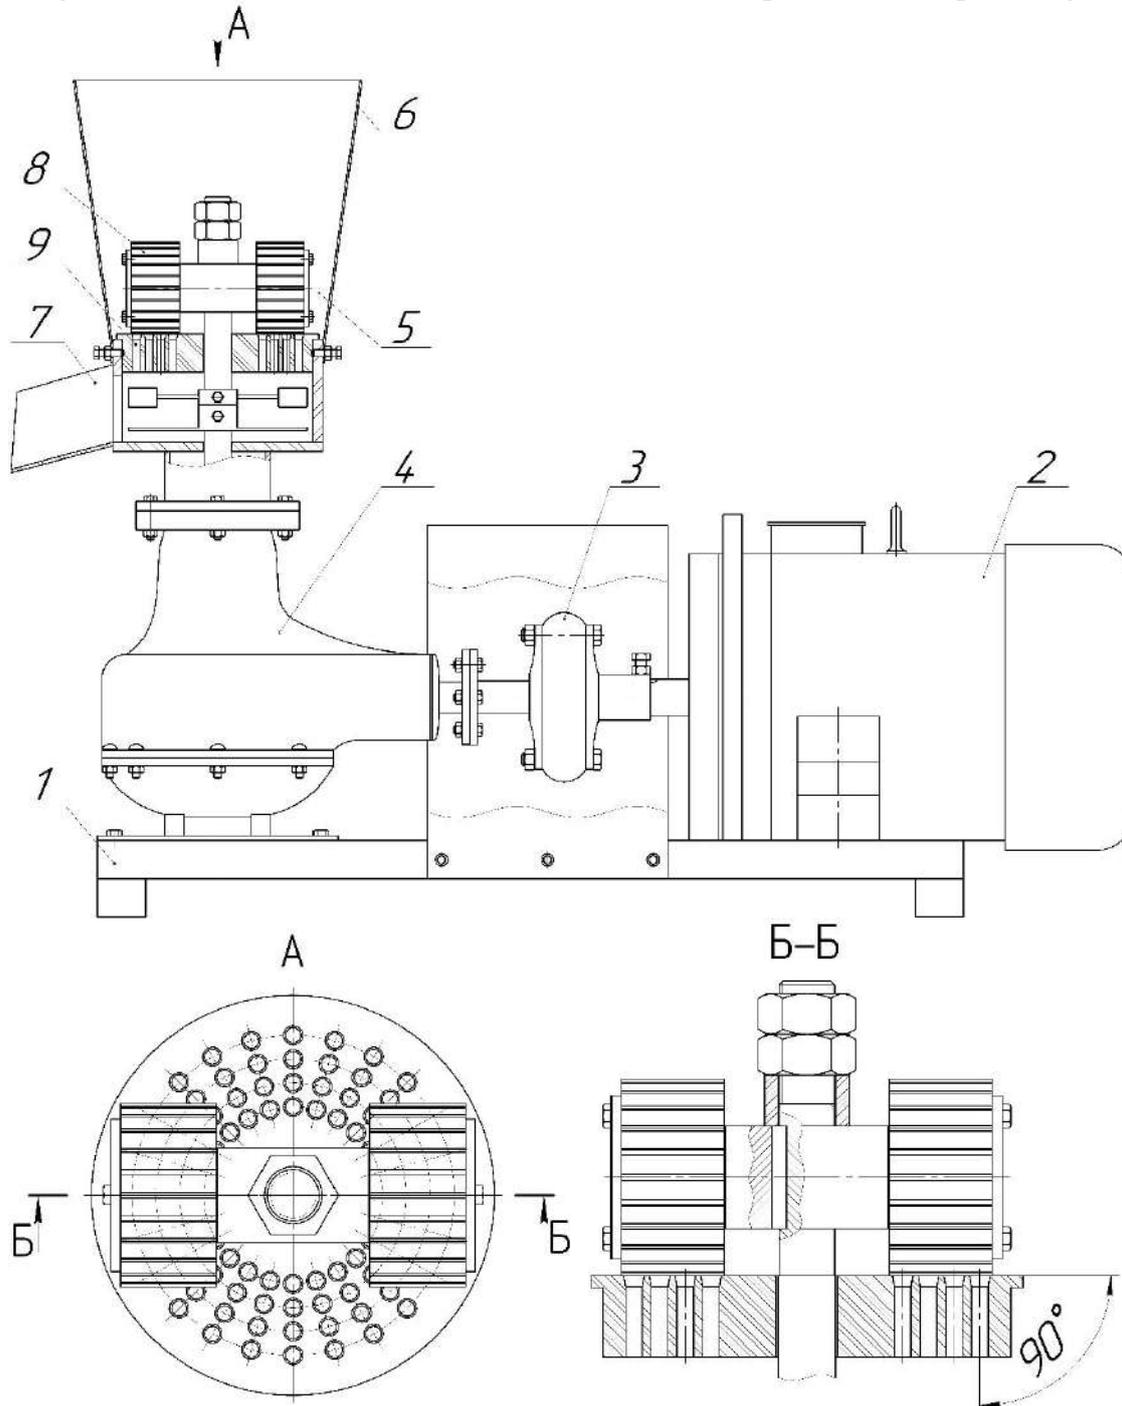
Конструктивно-технологічна схема установки для виготовлення пелет.
